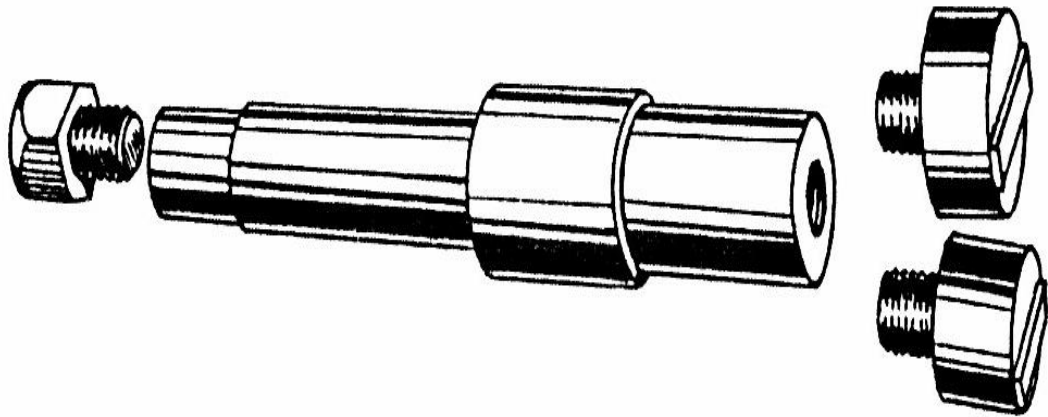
Оправка для ремонту поворотного кулака
